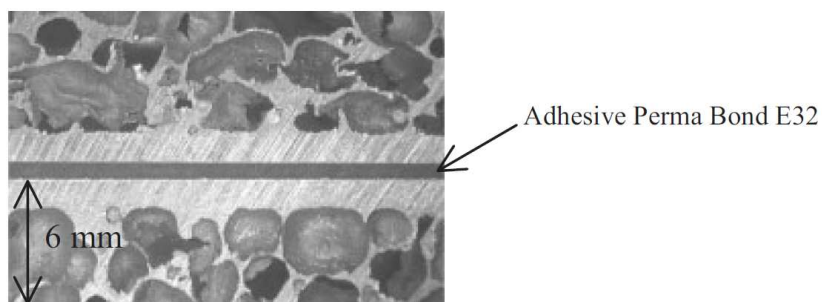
35 Esempio di giunzione adesiva su pannelli sandwich [See02]
